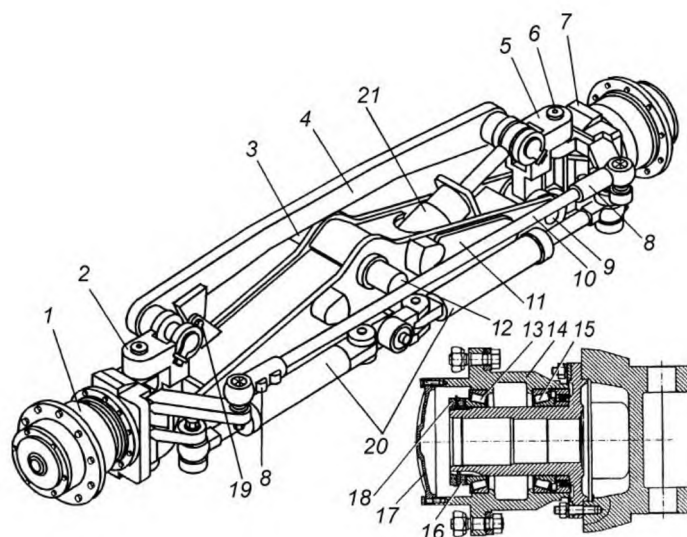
Передний мост: 1, 7 – ступицы; 2, 5 – поворотные рычаги; 3, 12 – оси; 4 – тяга; 6 – ось; 8 – наконечник; 9 – палец; 10 – поперечная тяга; 11 – балка; 13, 15 – подшипники; 14 – корпус; 16 – гайка; 17 – крышка; 18 – контргайка; 19 – стопорная ось; 20 – гидроцилиндры поворота колес; 21 – гидроцилиндр наклона колес
